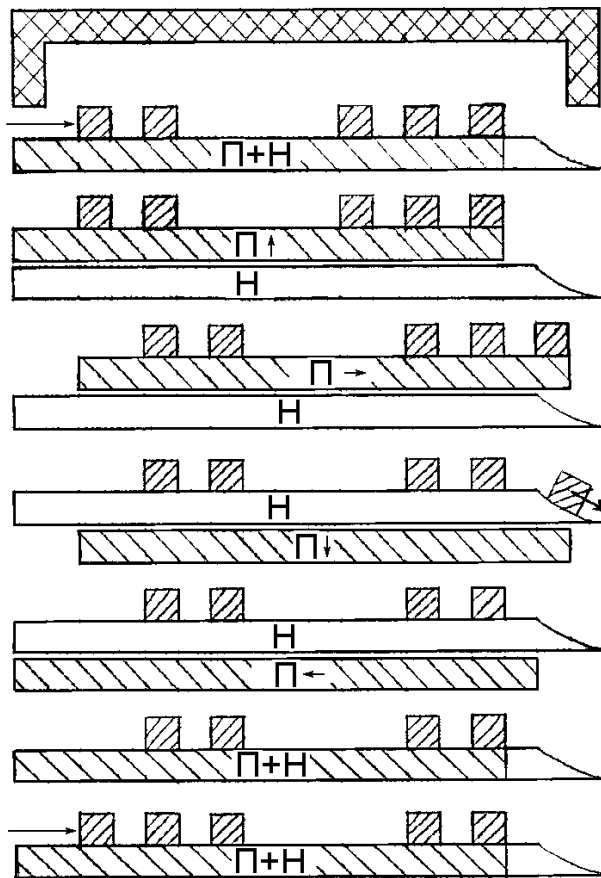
Схема транспортирования изделий в печах с подвижными балками
